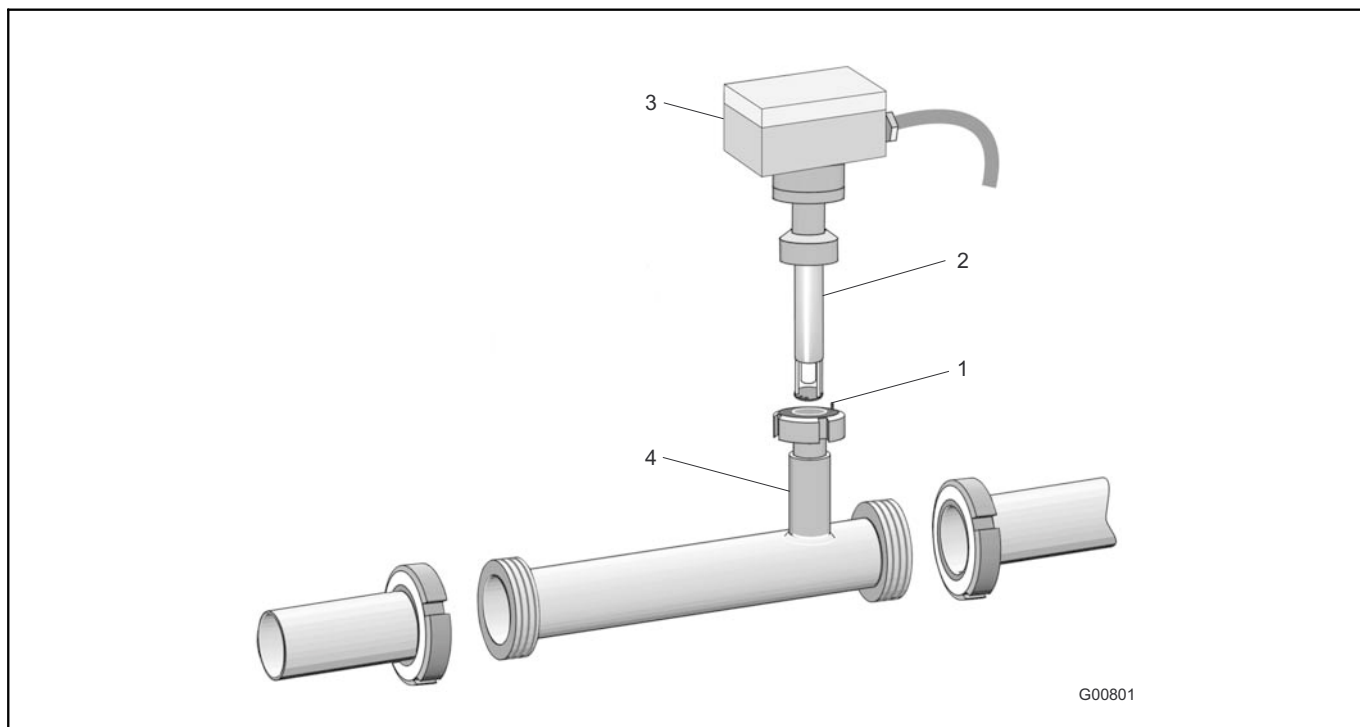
Prozessanschlüsse mit Rohrverschraubung S nach DIN11851. Messwertaufnehmer und Rohrbauteil auch mit FG-Flanschen möglich. FG-Flansche am Rohrbauteil sind immer beidseitig glatt (ohne Nut).
